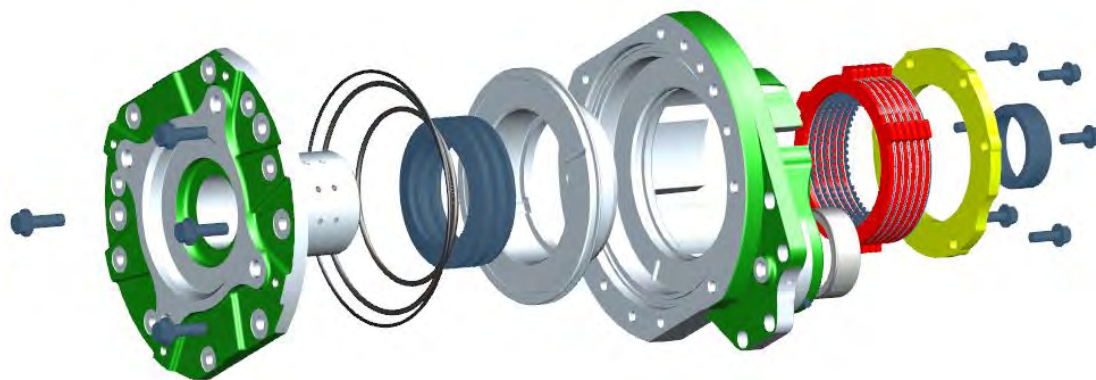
"Explosionado del montaje del freno de estacionamiento"
